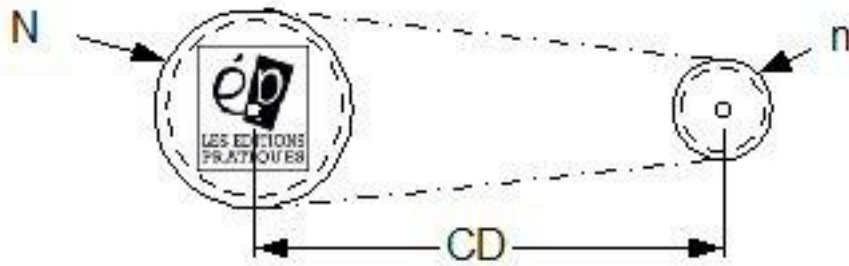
DIMENSION DE TRANSMISSION PAR CHAÎNE
